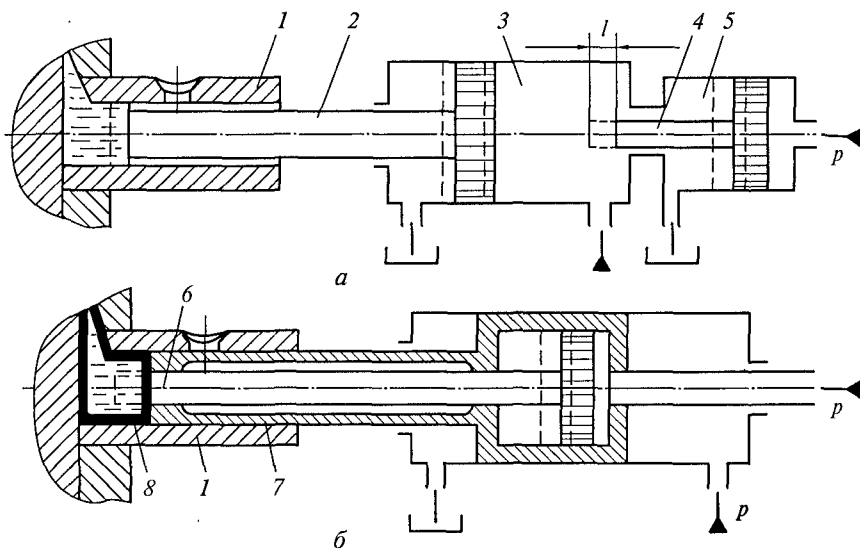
Схемы механизмов прессования машин литья под давлением: *а* — с мультипликатором; *б* — с двойным плунжером; 1 — камера прессования; 2 — шток основного гидроцилиндра с пресс-поршнем; 3 — основной гидроцилиндр; 4 — шток мультипликатора; 5 — мультипликатор; 6 — дополнительный плунжер; 7 — основной плунжер; 8 — затвердевший металл; *l* — ход мультипликатора; *p* — давление
